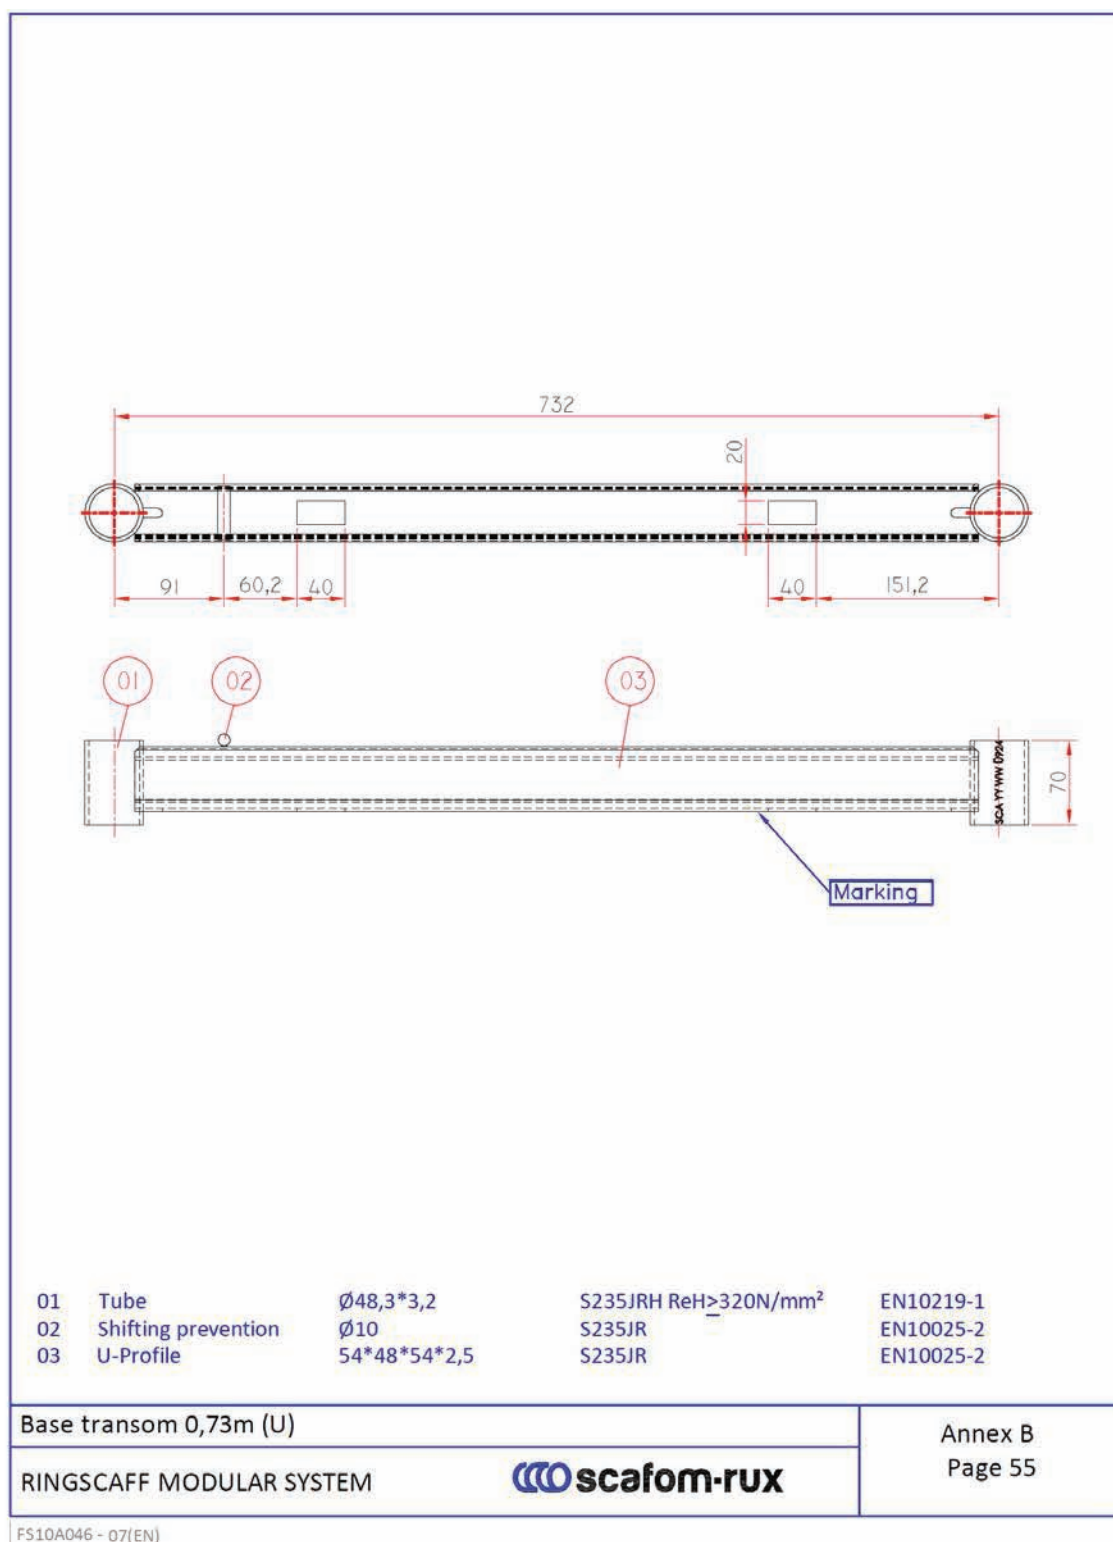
Travessa 0,73 m, secção em U (variante 2)
